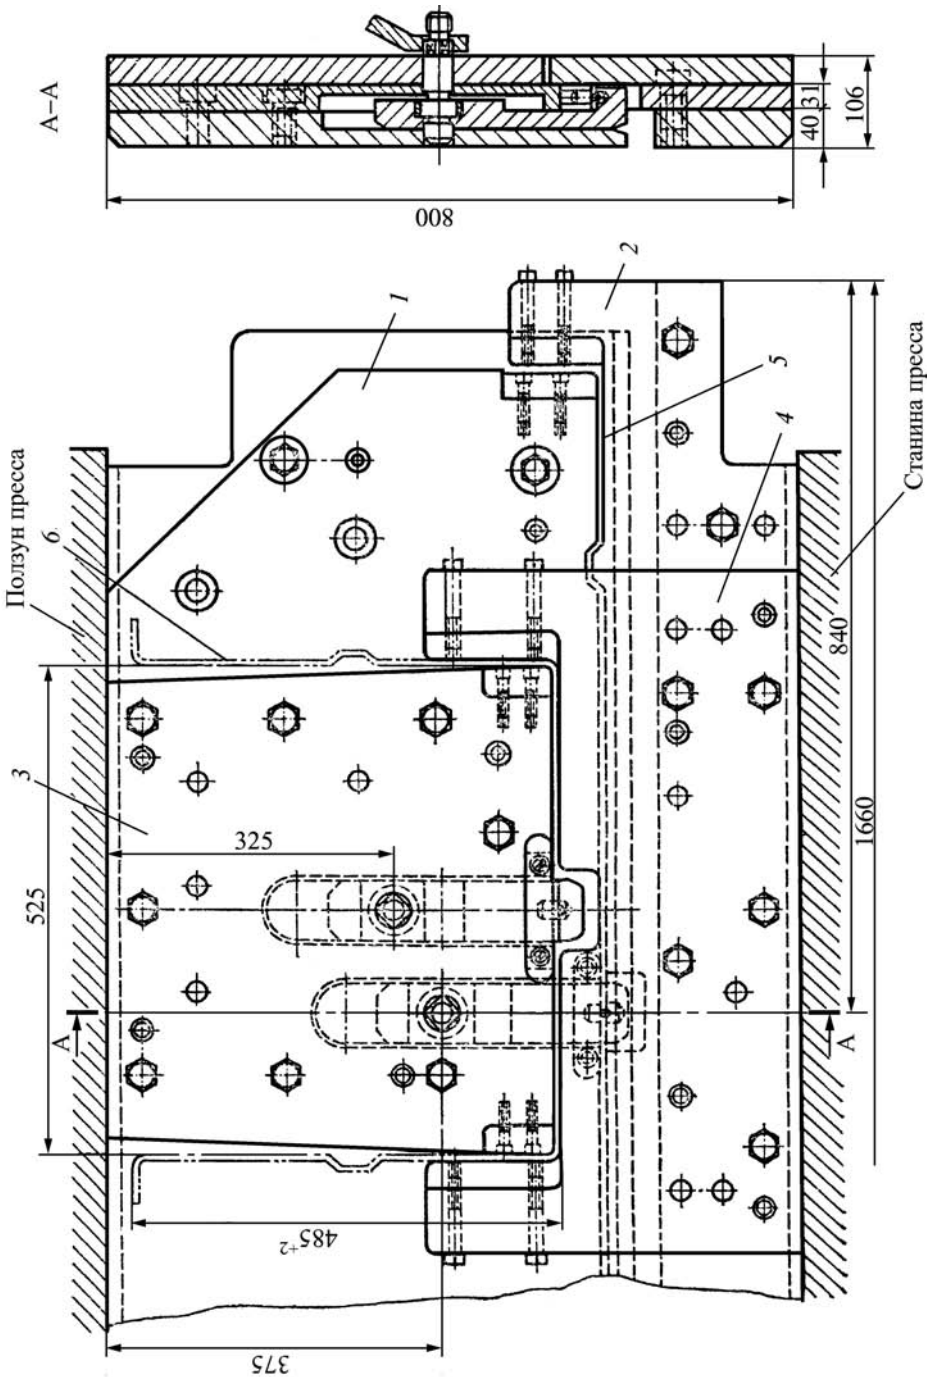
Штампы для двухпереходной гибки П-образной детали:
